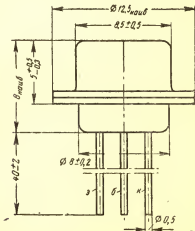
Габаритный чертеж транзисторов П29 — П30.
